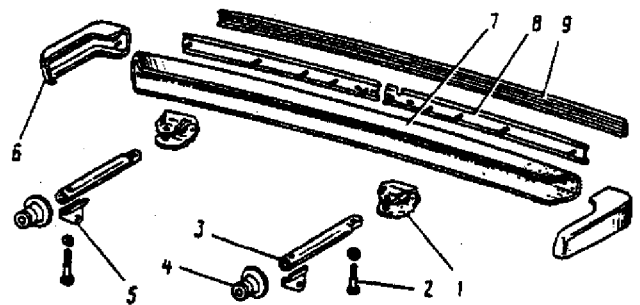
Conjunto do pára-choque dianteiro: 1 - suporte; 2 - parafuso de fixação; 3 - suporte de fixação; 4 - vedação de borracha; 5 - aba de apoio do suporte; 6 - ponteiras plásticas; 7 - pára-choque; 8 - suporte da guarnição; 9 - guarnição.
